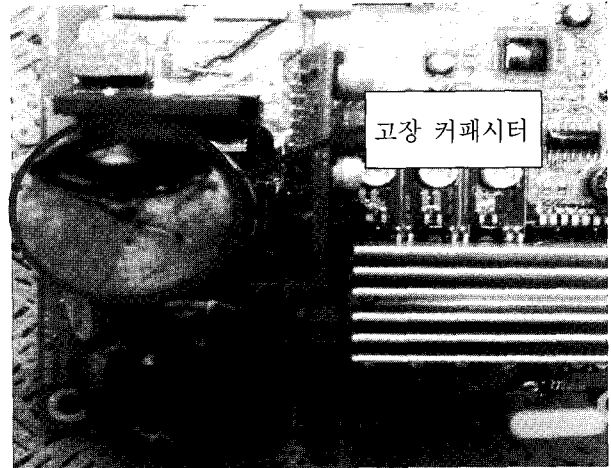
PCB 제조 과정에서의 오염으로 인한 전해 커패시터의 고장 사례
